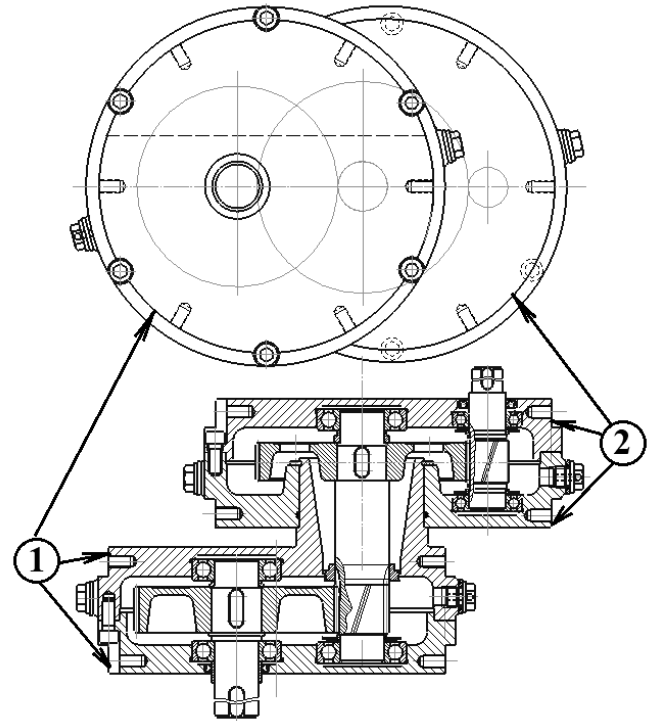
Цилиндрические поверхности 1 и 2 с резьбовыми отверстиями для опор.
